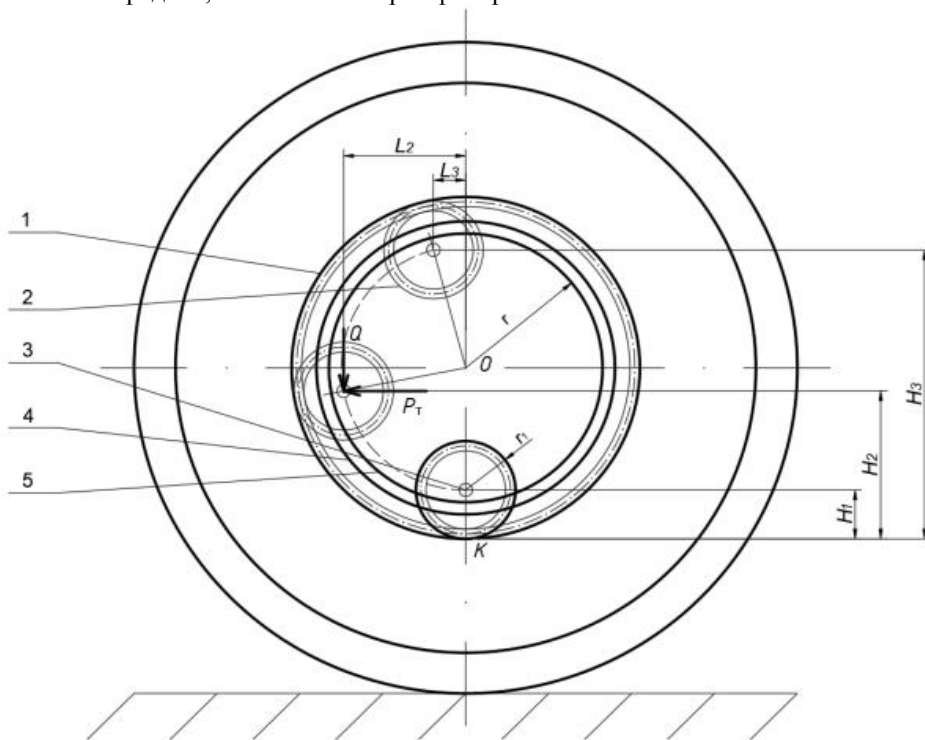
Схема колеса с планетарным редуктором – дифференциалом
